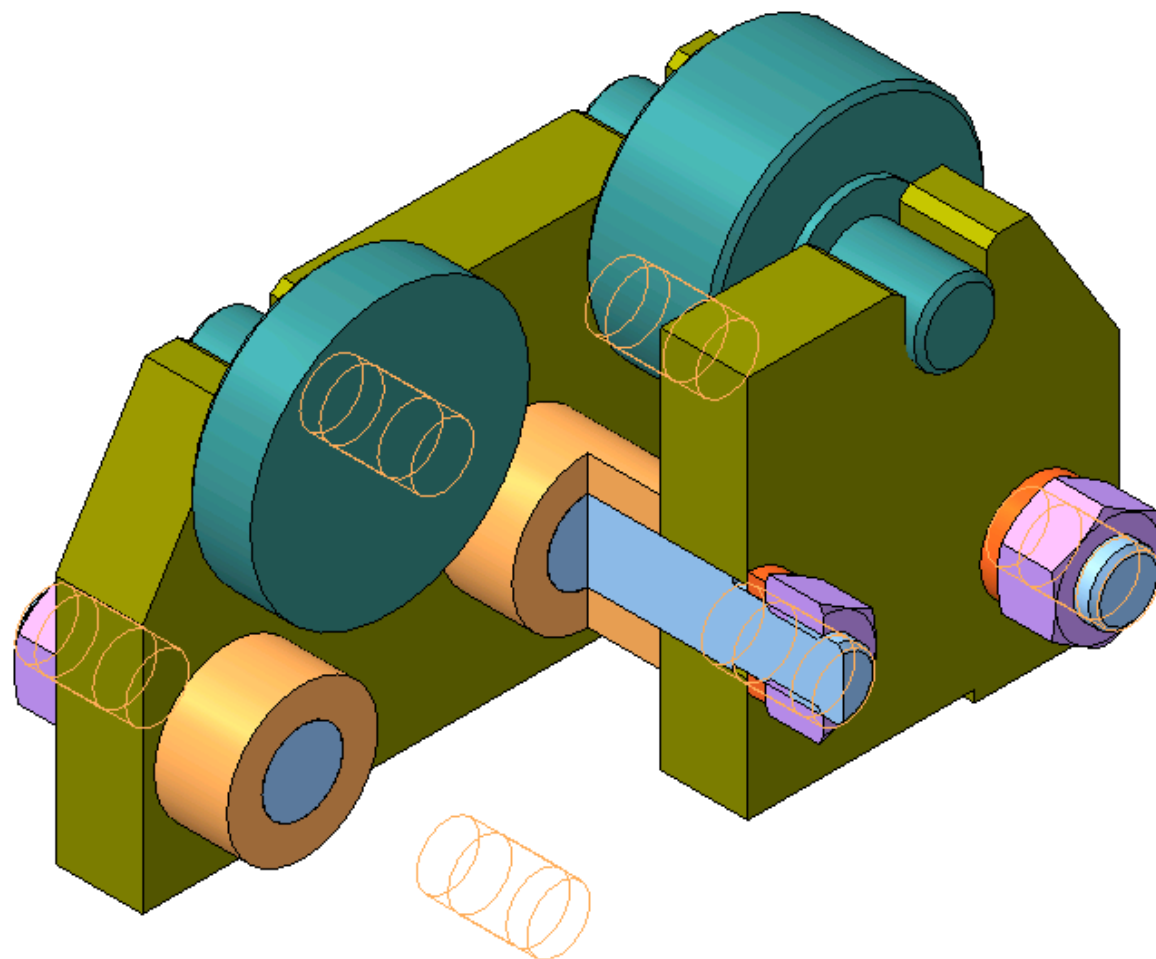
3D-модель сборки изделия «Опора роликовая» (варианты 13, 33)
